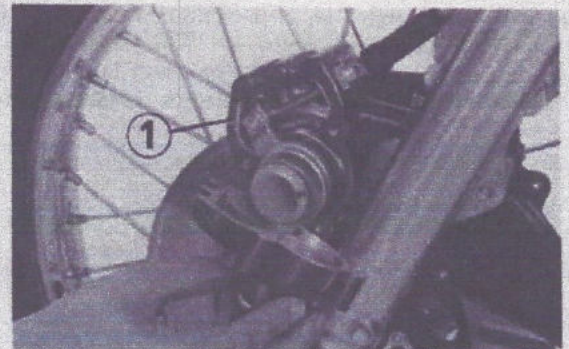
(1) Joint d'étanchéité de couvercle de l'étrier
